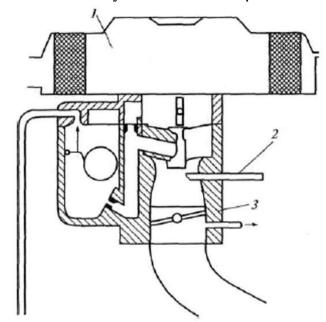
Схема подачи газа через штуцер: 1 - воздушный фильтр; 2 - штуцер для подвода газа; 3 - корпус карбюратора
